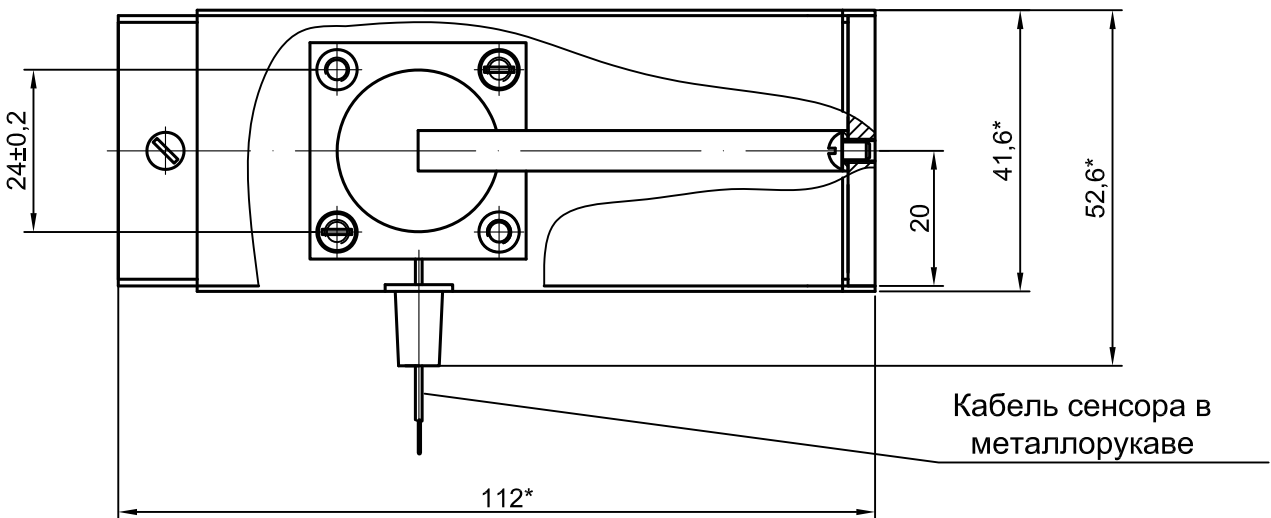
Габаритные размеры сенсора СПВ-1Г с узлом крепления
